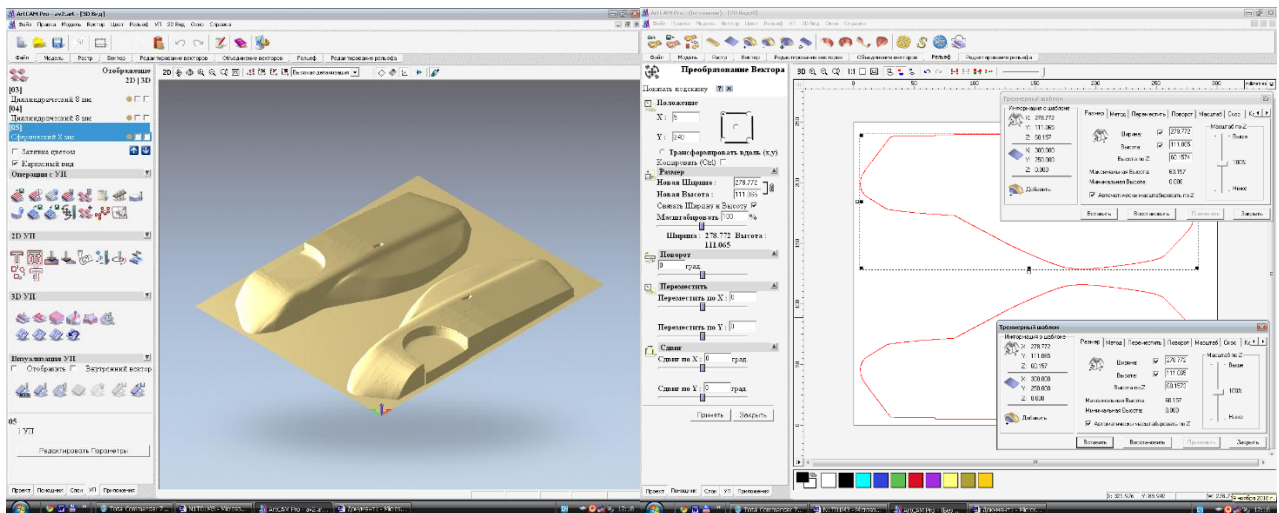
розташування зовнішніх частин на робочій площині
